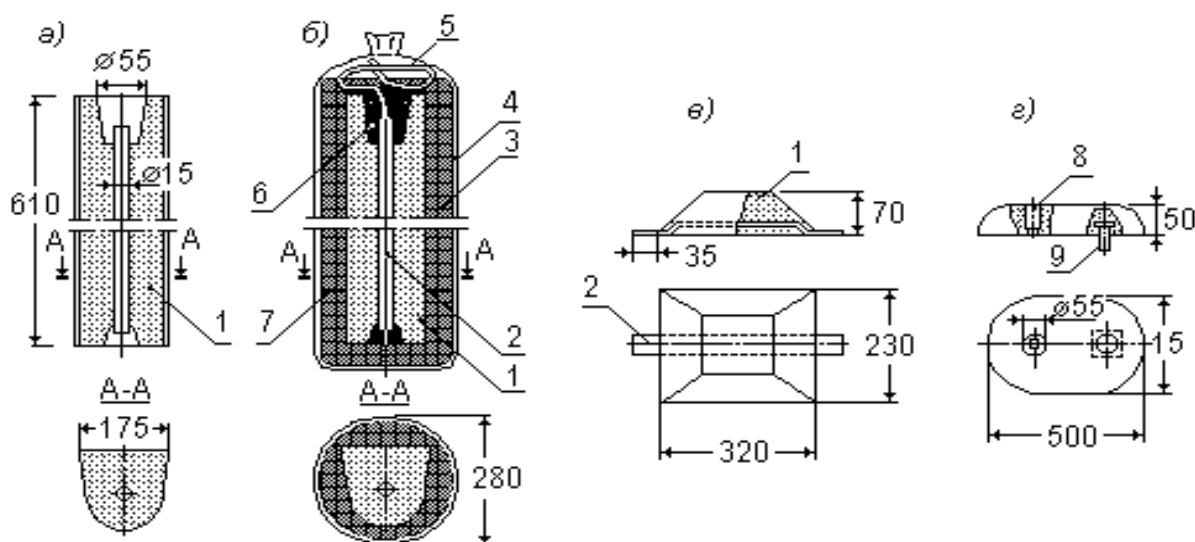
Конструкции протекторов: а- стержневой магниевый типа ПМ-20; б-стержневой с активатором типа ПМ-20У; в- плоский алюминиевый типа П-КОА-10; г - плоский алюминиевый типа П-РОА-9. 1- тело протектора; 2 - стальной стержень; 3 - активатор в хлопчатобумажном мешке; 4 - мешок бумажный; 5 - провод изолированный 10 м; 6 - битумно-резиновая масса; 7 - шайба фанерная; 8 - отверстие крепежное; 9 - контактный болт.
